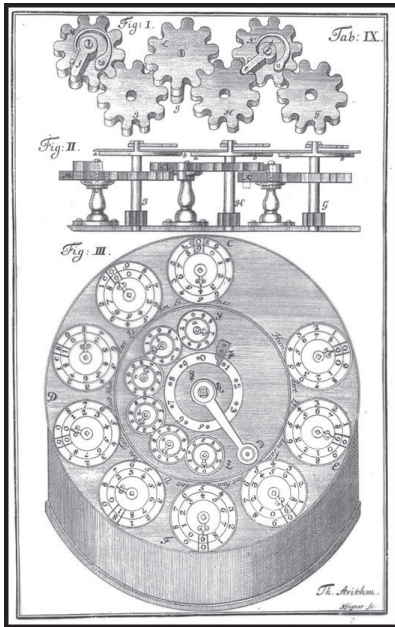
Zeichnung der Leupoldschen Rechenmaschine
